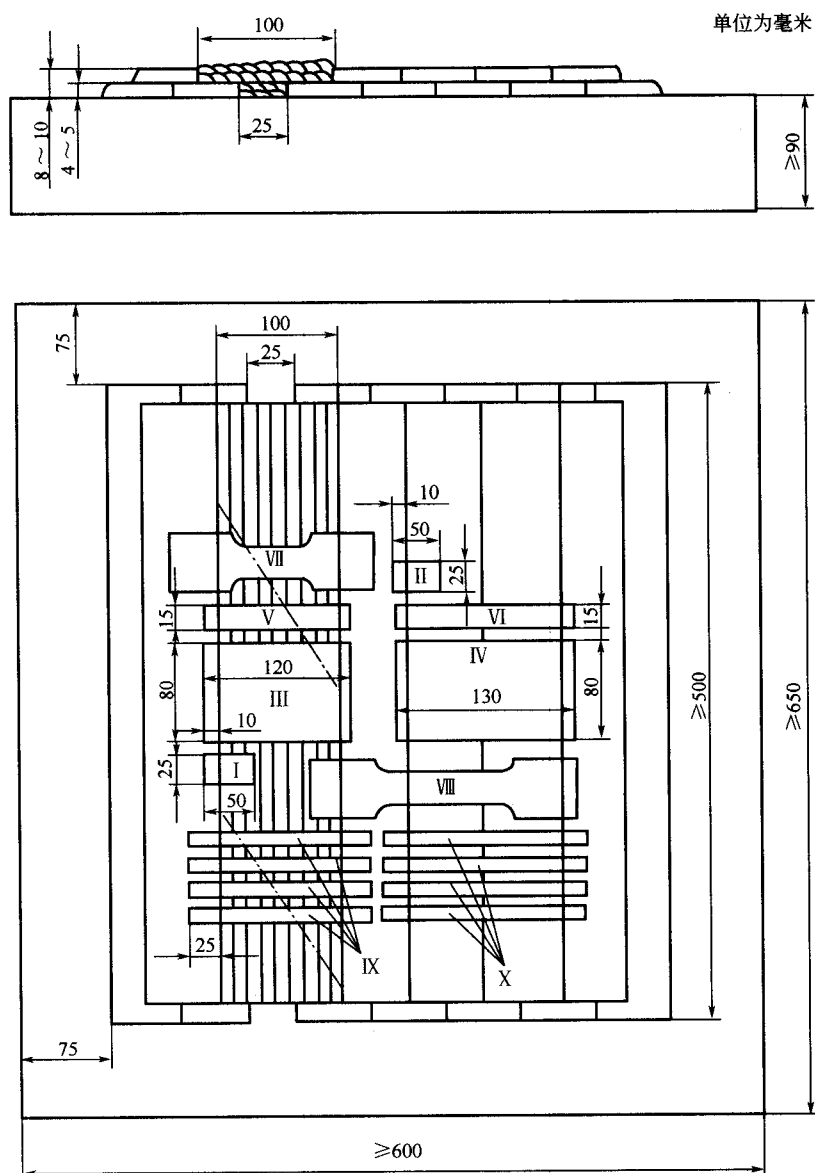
带极-焊条电弧焊堆焊工艺评定试板尺寸及取样示意图
